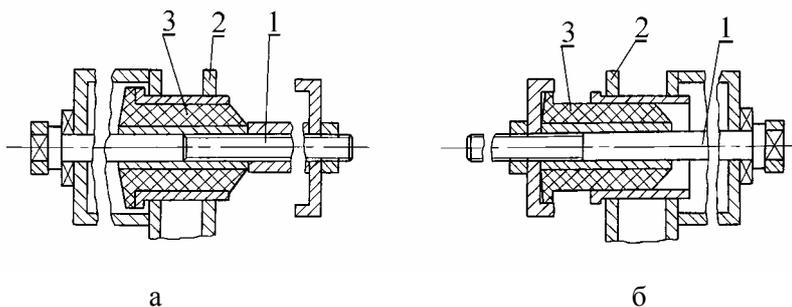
Схема выпрессовки (запрессовки) шарнира рычага задней подвески:
